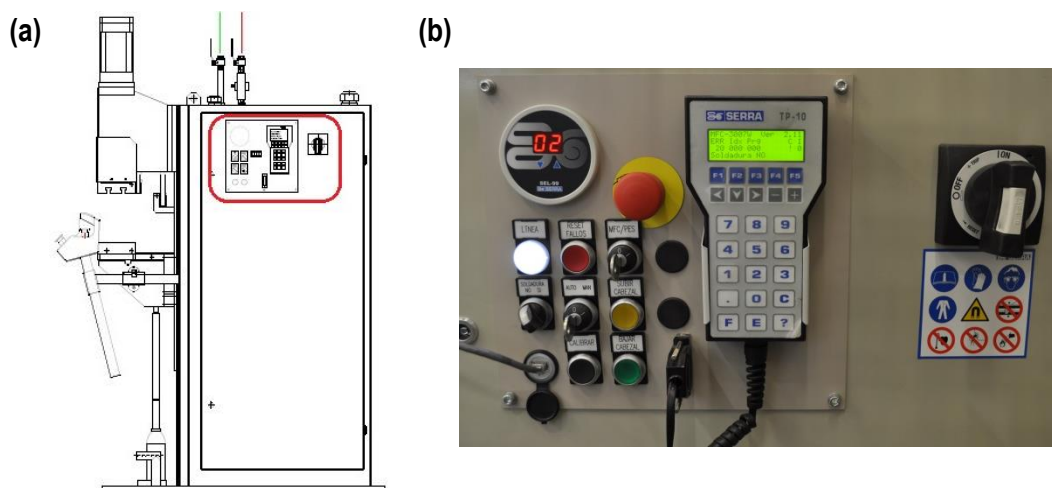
a) Ubicación y b) detalle de la carátula de maniobra de la máquina de soldadura.
